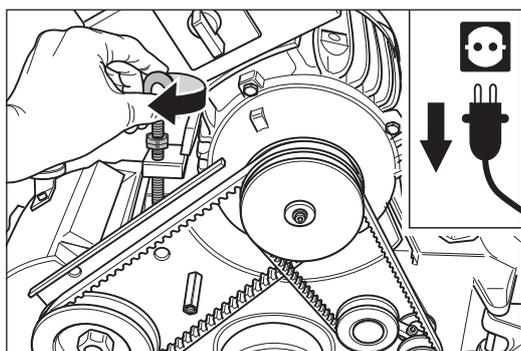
Die beiden Keilriemen auflegen und zum Spannen die Ringschraube am Motor im Uhrzeigersinn drehen.
